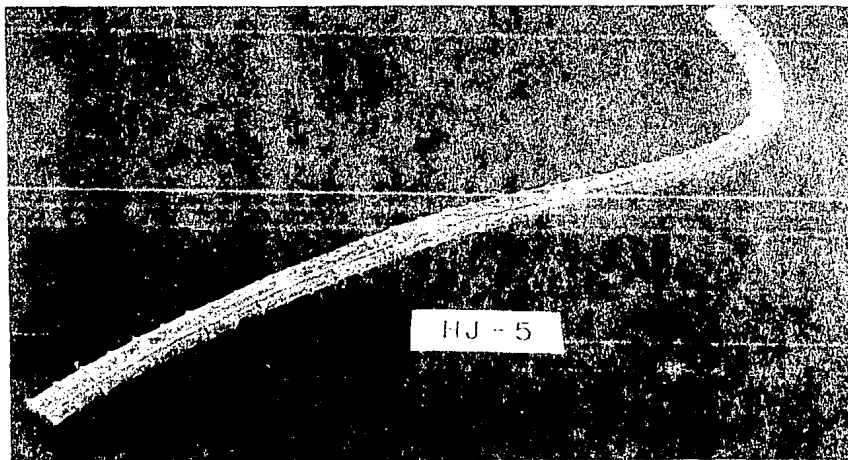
MUESTRA HJ-5, LA FRACTURA SE ENCUENTRA EN LA PARTE INFERIOR IZQUIERDA DE LA FOTOGRAFIA.
